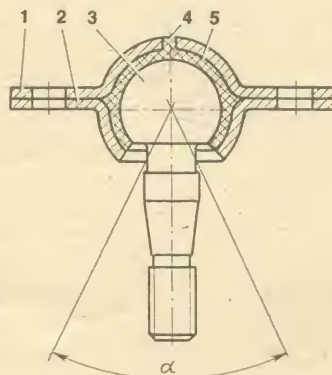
Шарнир ВАЗ-2108: 1, 2 — верхняя и нижняя части сварного корпуса; 3 — шаровой палец; 4 — слой термореактивной смолы; 5 — слой тефлоновой ткани; α — угол качения пальца относительно корпуса.
